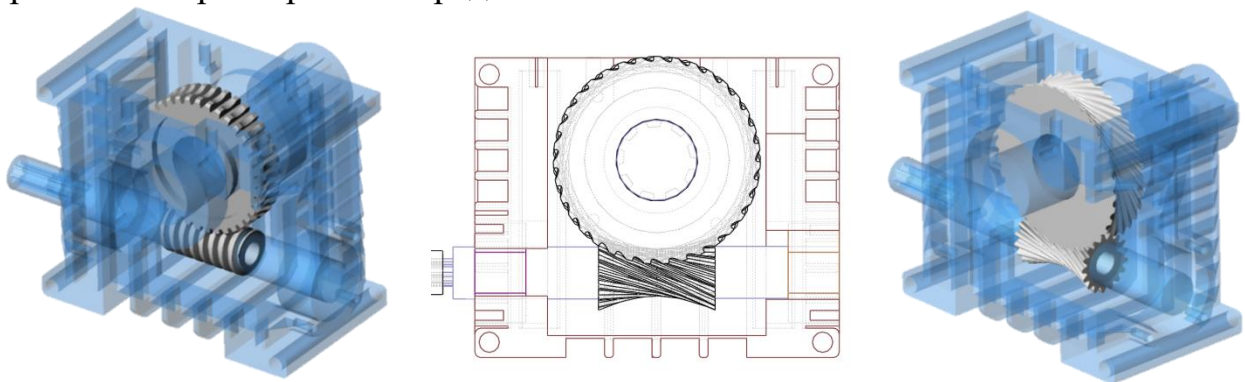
Комп'ютерна модель черв'ячного редуктора і редуктора з розробленою просторовою передачею
